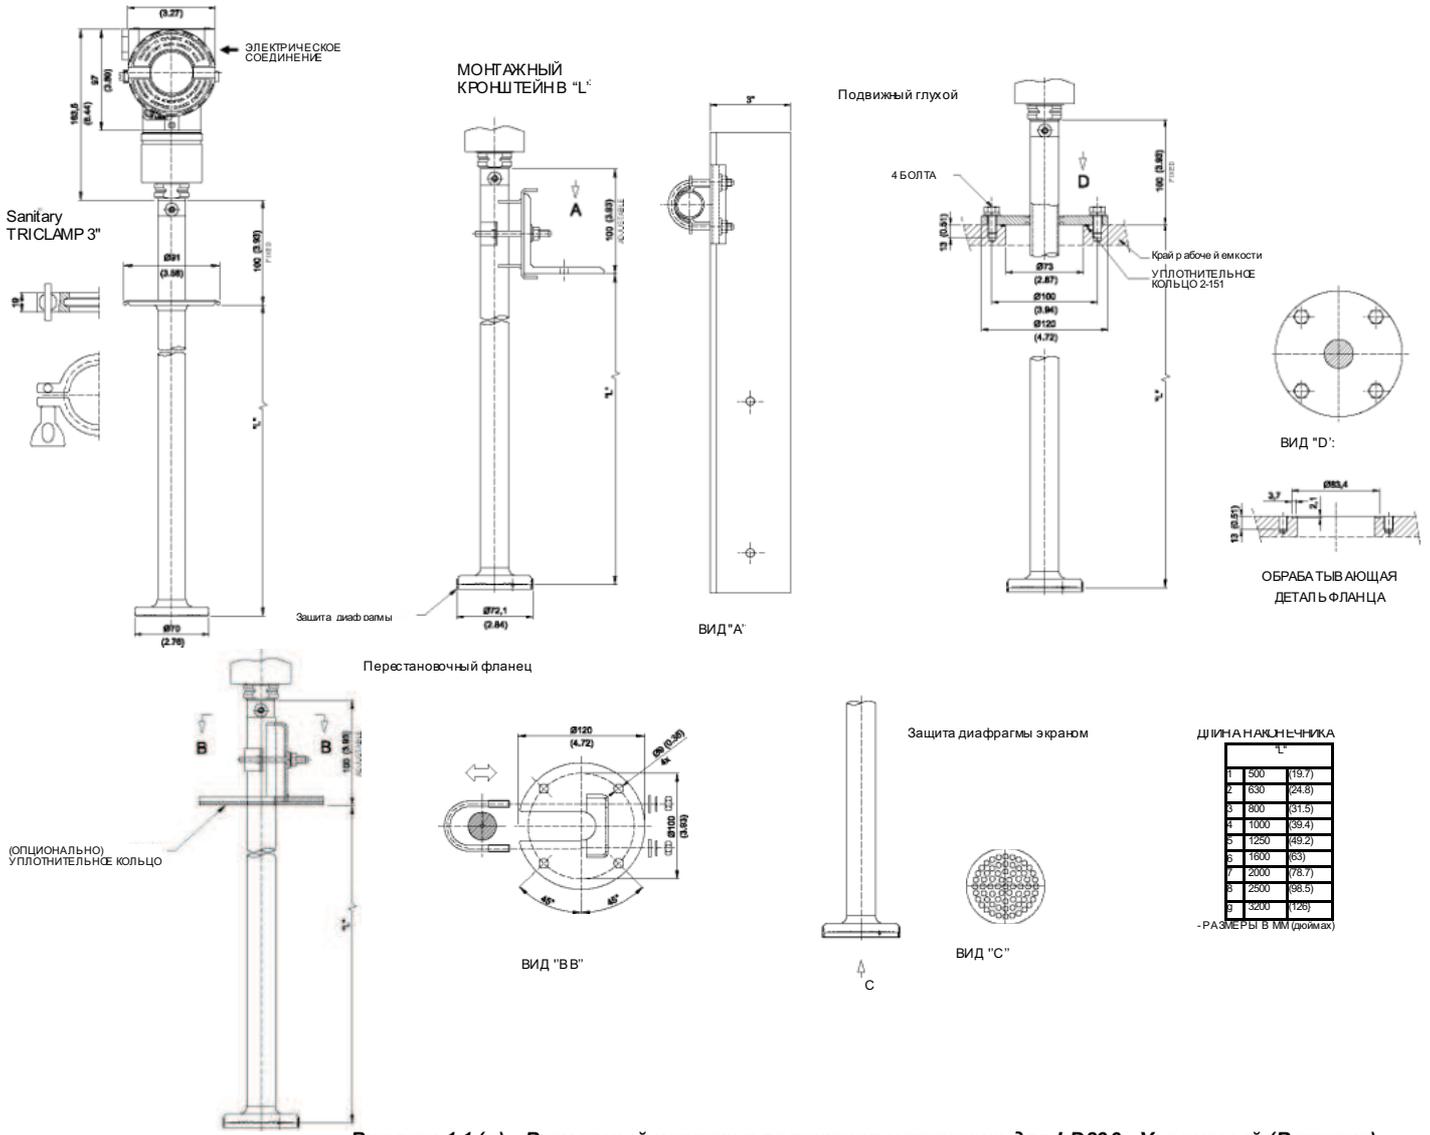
(е) - Размерный чертёж и положения установки для LD290 - Уровневый (Вставка)
